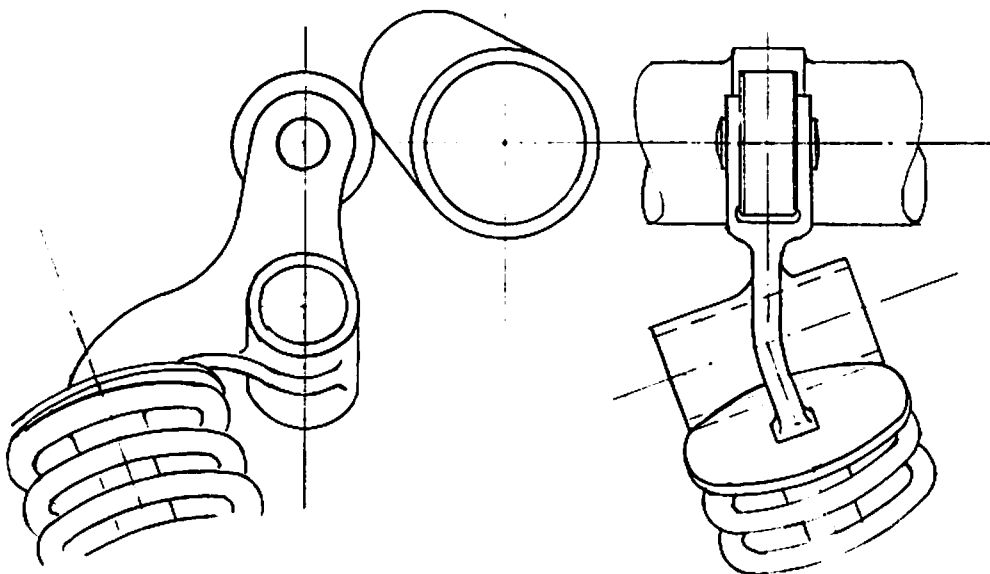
Steuerung eines schräg angeordneten Ventils durch einen Winkelhebel.
